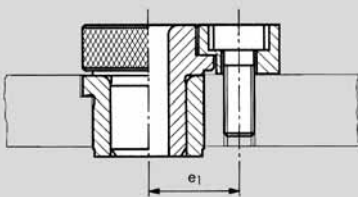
Schnellwechslbuchse Form K mit eingelassener Bundbohrbuchse DIN 172 oder zylindrischer Bohrbuchse DIN 179. Die Befestigung erfolgt mit Spannbuchse DIN 173 und Zylinderschraube DIN 912. Die Schnellwechslbuchse Form K kann auch mit Anschlagstift gesichert werden. Diese Befestigungsmöglichkeit ist nicht für langspanende Werkstoffe vorzusehen (Unfallgefahr).
